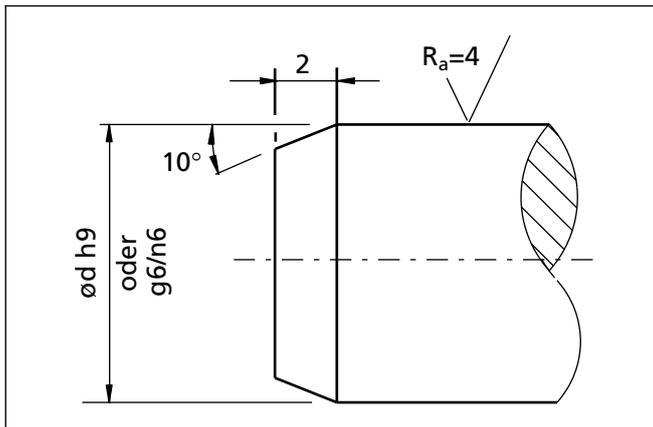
Durchmesser tolerance, Oberflächenrauheit und Kantenfäse der Welle
